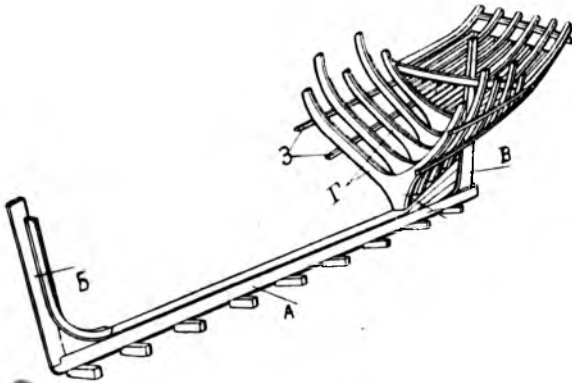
Строение корпуса деревянной лодки крейсерского типа.—А, киль.—Б, форштевень (передний брус).—В, задний брус (ахтерштевень).—Г, шпангоуты.—З, продольные соединительные планки между шпангоутами.
